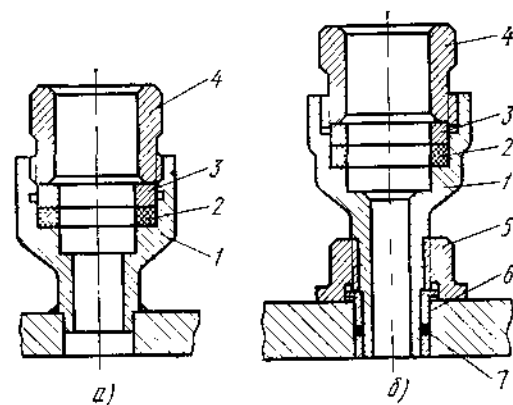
Схемы бесфланцевых грибковых соединений с резиновыми уплотнителями
